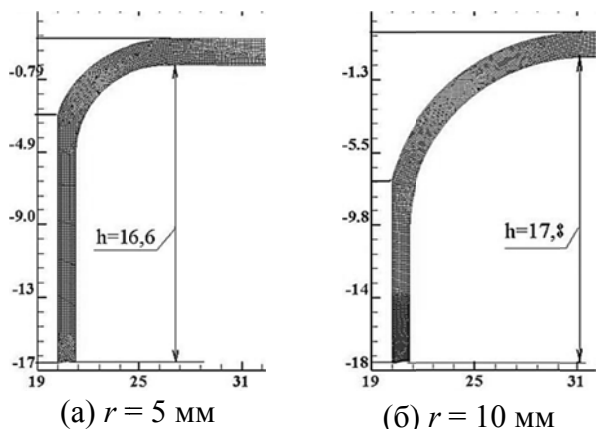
Геометрична форма відбортеної частини заготовки в матриці з різним радіусом заокруглення  $r$
